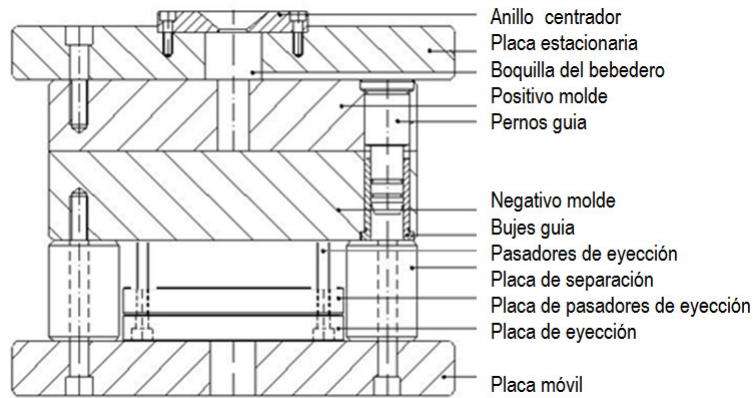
Componentes de un molde de inyección (Modificada de [6]).
